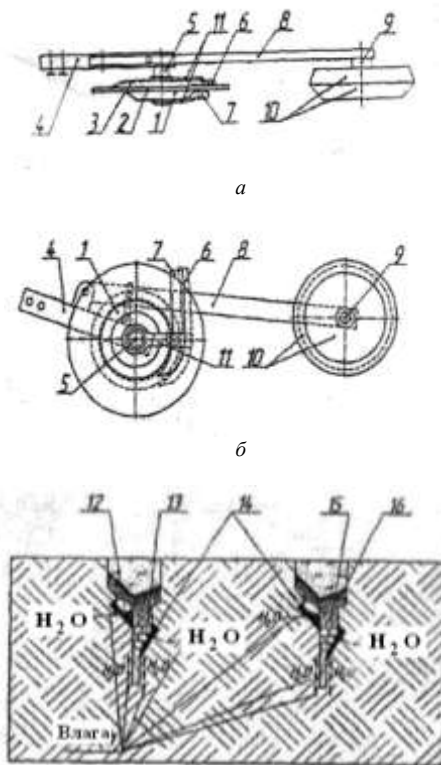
Комбинированный двухдисковый сошник с конусными ребрами и нулевым углом атаки дисков: *а* – вид сверху; *б* – вид сбоку; *в* – вид сзади; 1 – плоские диски; 2 – реборды-бороздкообразователи; 3 – корпус; 4 – ось; 5 – семянаправители; 6 – пластины; 7 – козырьки
